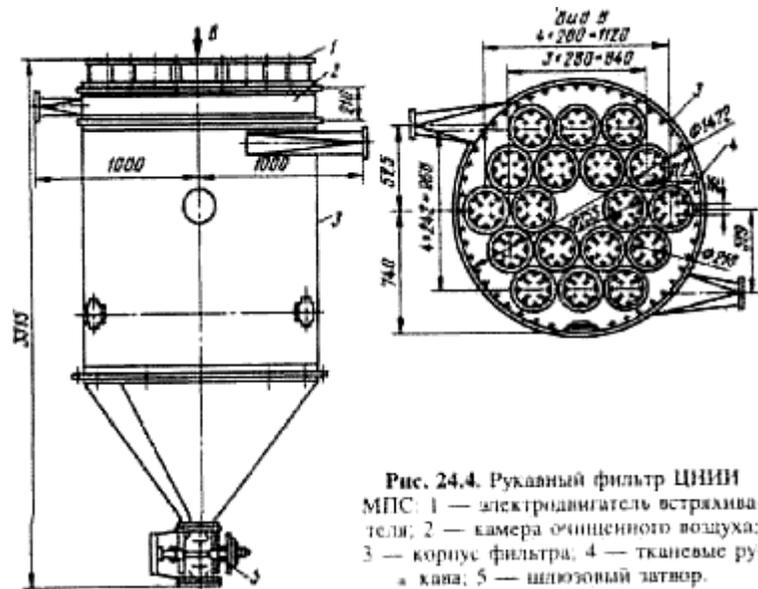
Рукавный фильтр ЦНИИ МПС: 1 — электродвигатель встраиваемый; 2 — камера очищенного воздуха; 3 — корпус фильтра; 4 — тканевые рукава; 5 — шиберный затвор.
